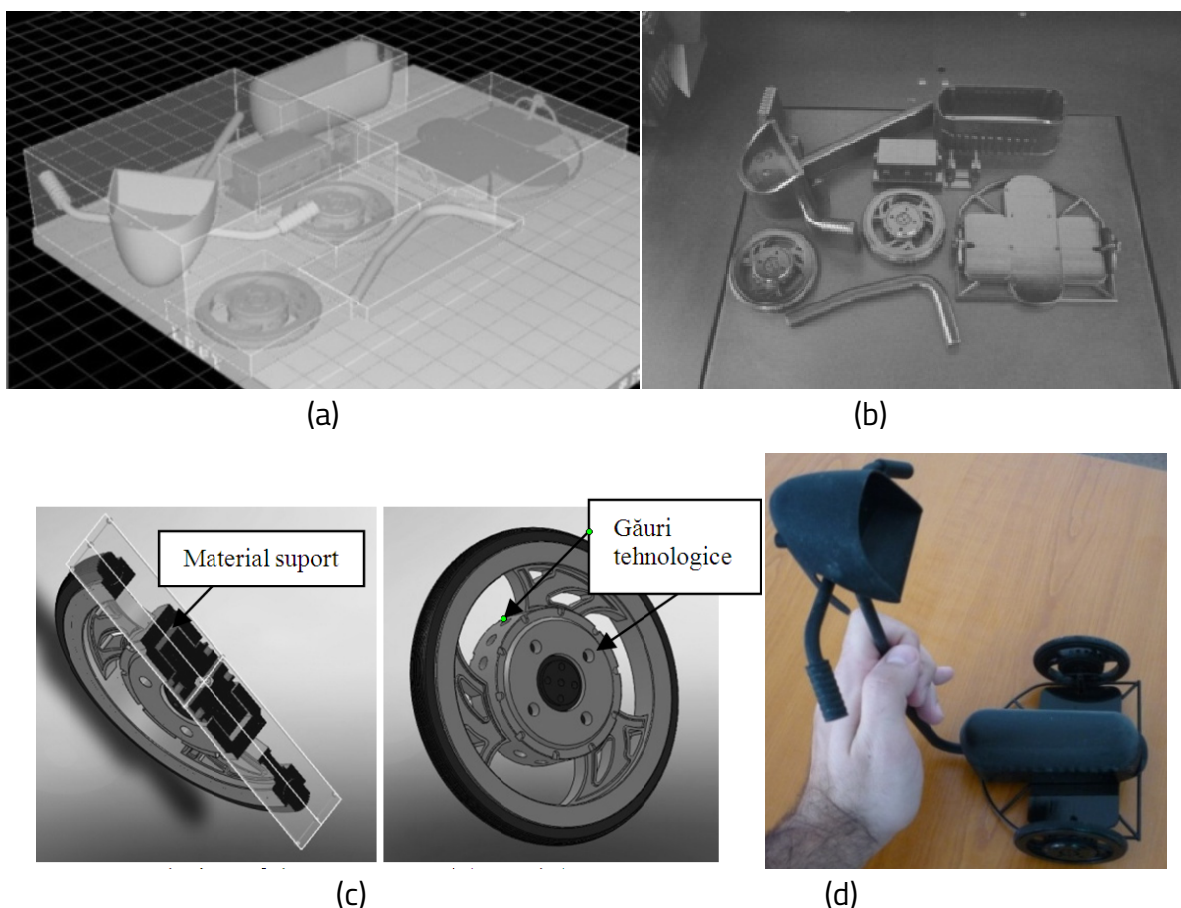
Produs realizat din mai multe componente: (a) simularea fabricației, (b) componentele fabricate aditiv, (c) designul rotii, (d) produsul asamblat [23].
